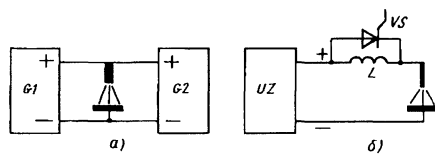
Способы формирования импульсов сварочного тока:
